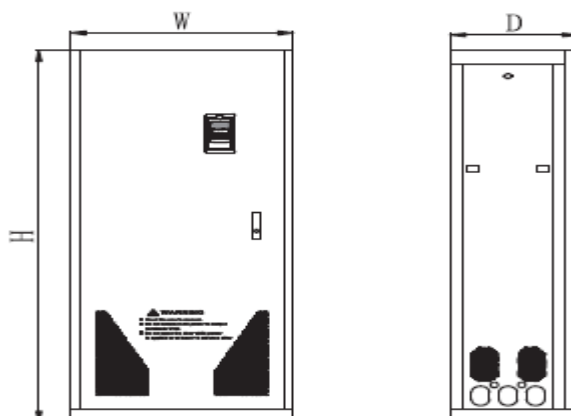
Чертеж с габаритными размерами преобразователя (модель С)
